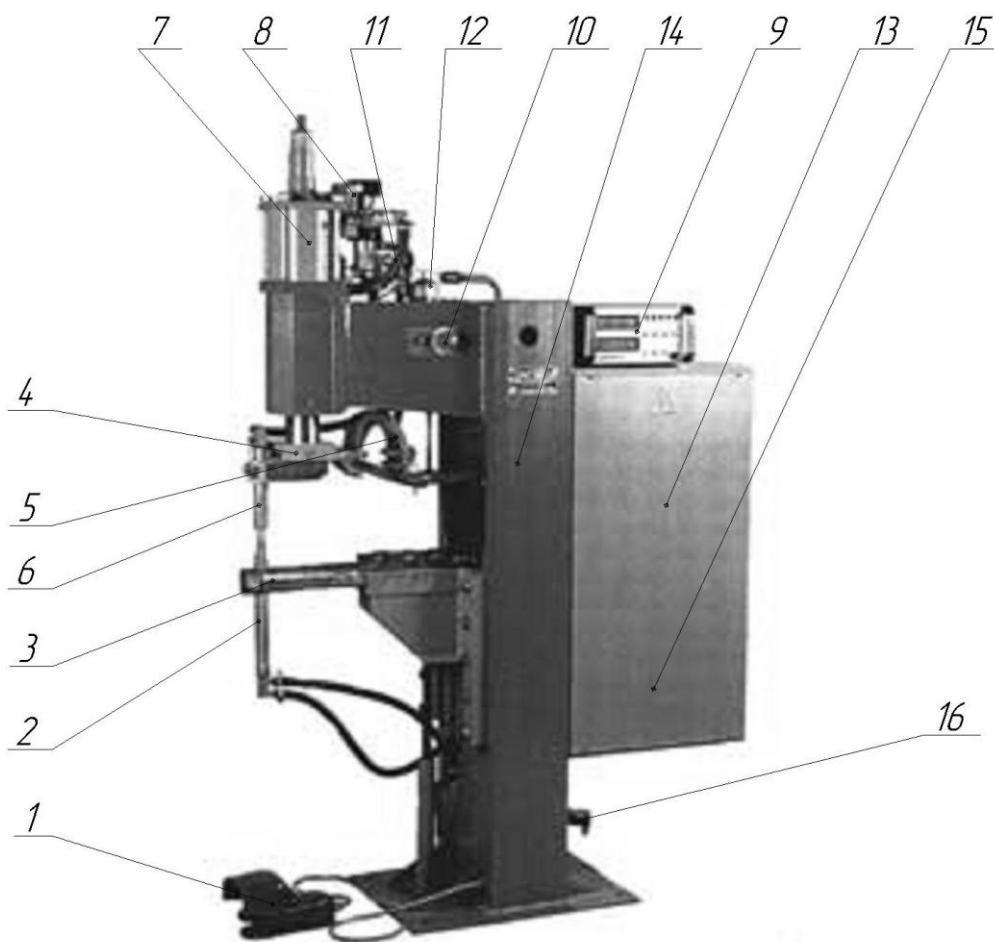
Контактная сварочная машина МТ-1932
